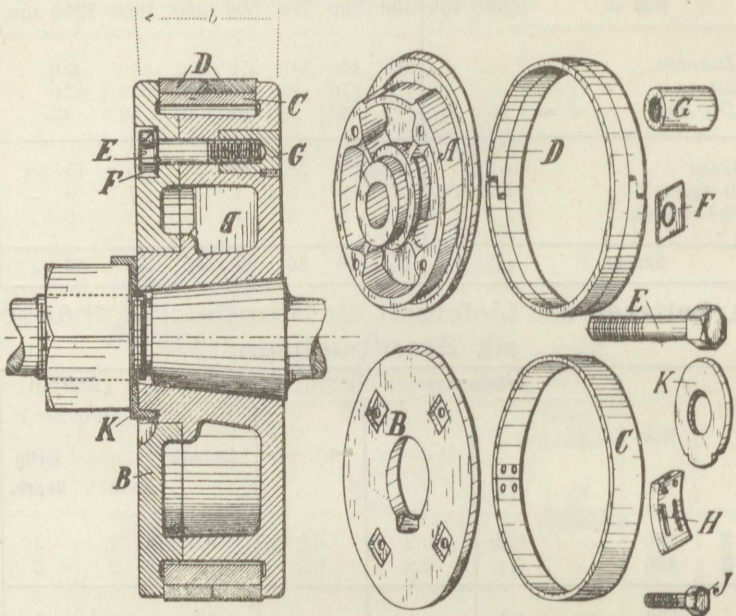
71. Dampfkolben für Maschinen über 400 Cylinderdurchmesser.
